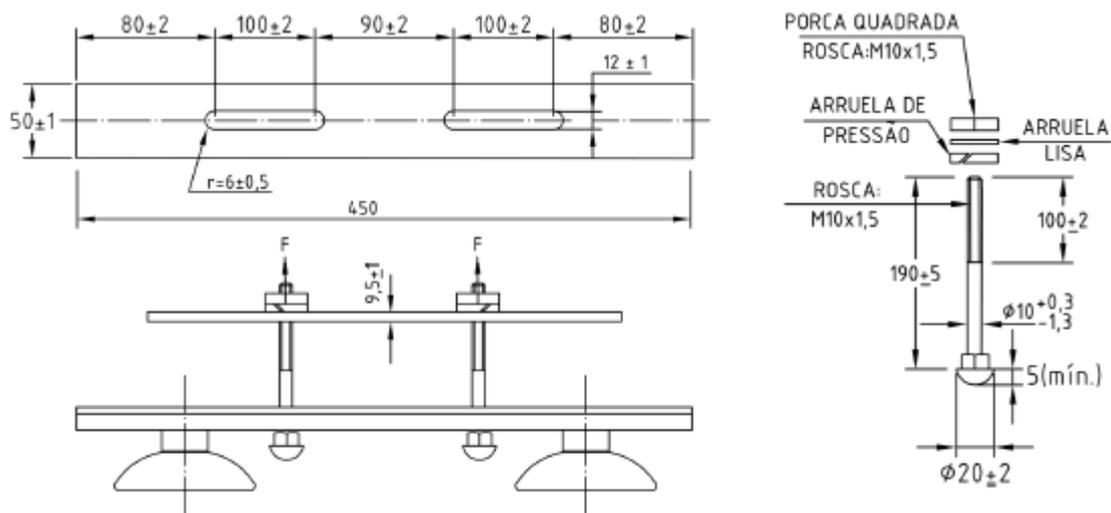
Suporte para Instalação de Seccionadora Unipolar – Tipo 2
